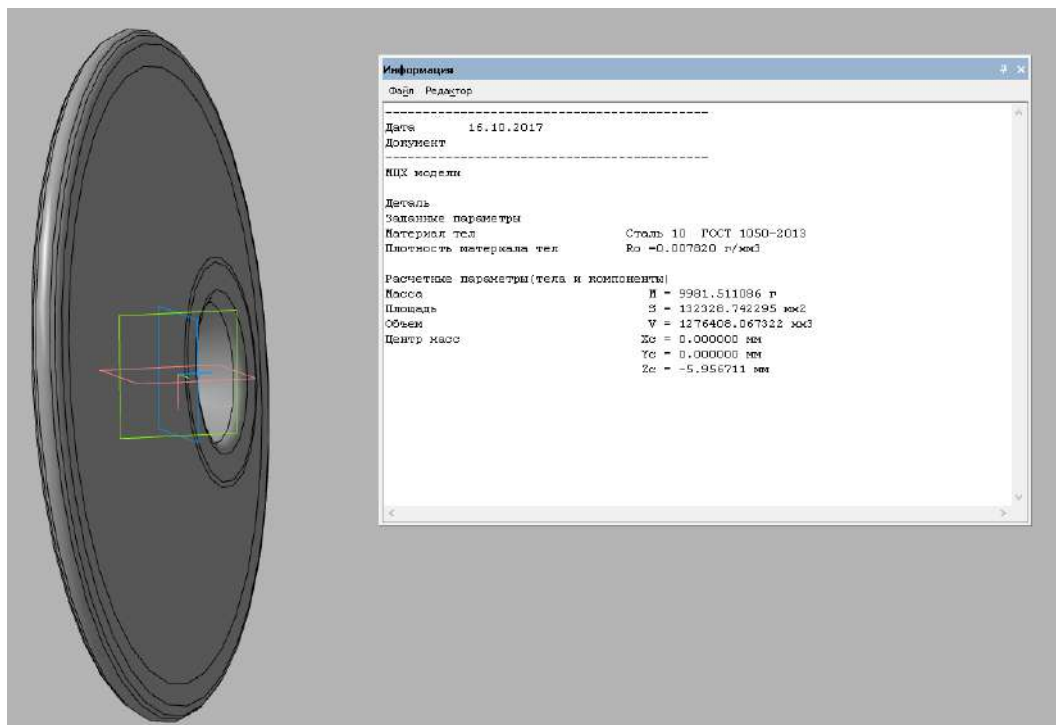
Модель штампованой заготовки на КГШП
